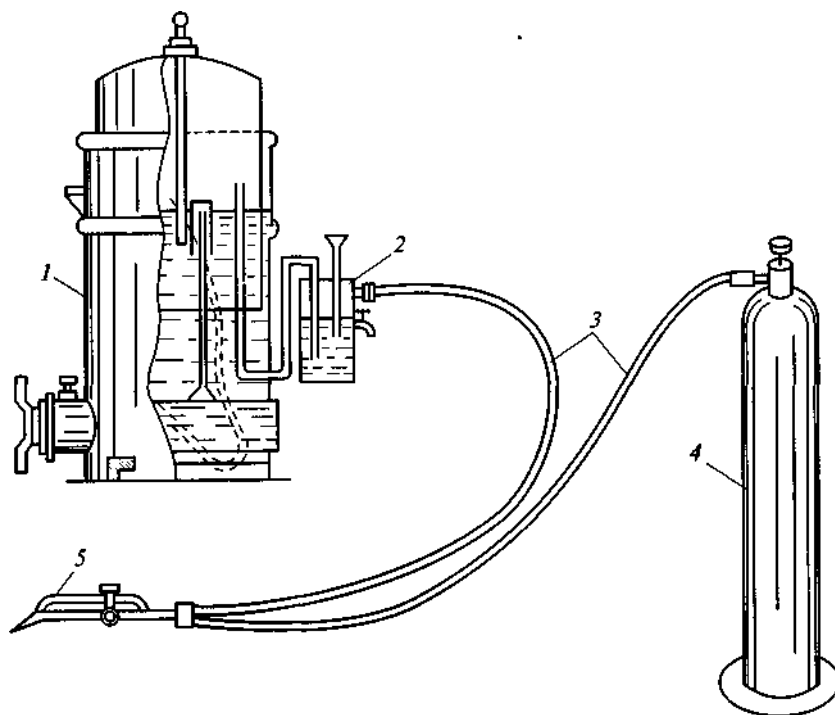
Установка для газовой сварки и резки металлов:
